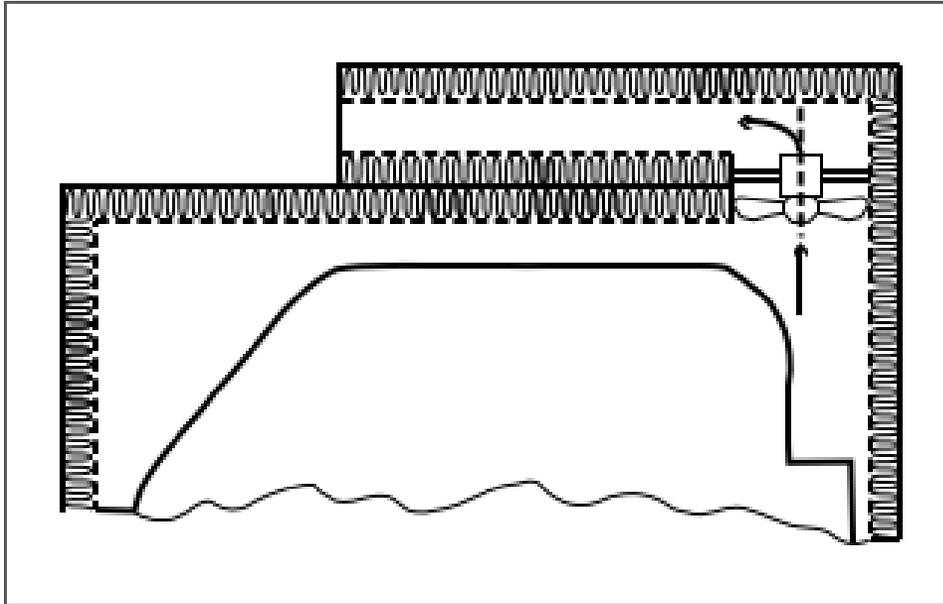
Entlüftungsöffnung einer Kapsel mit angeschlossener Schalldämpferstrecke
